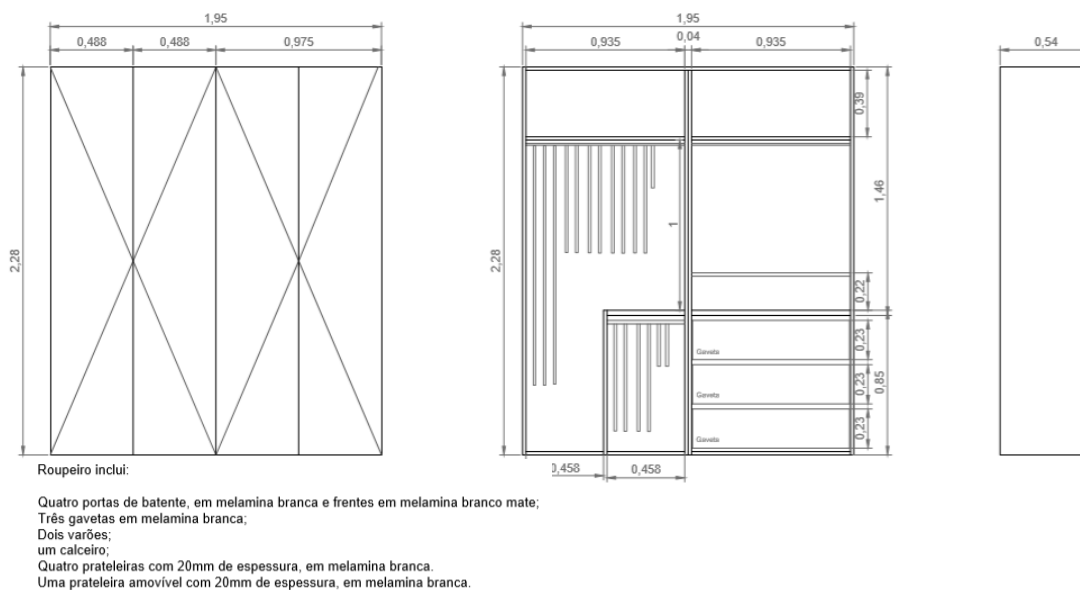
Desenho Técnico Roupeiro. Fonte: autor
